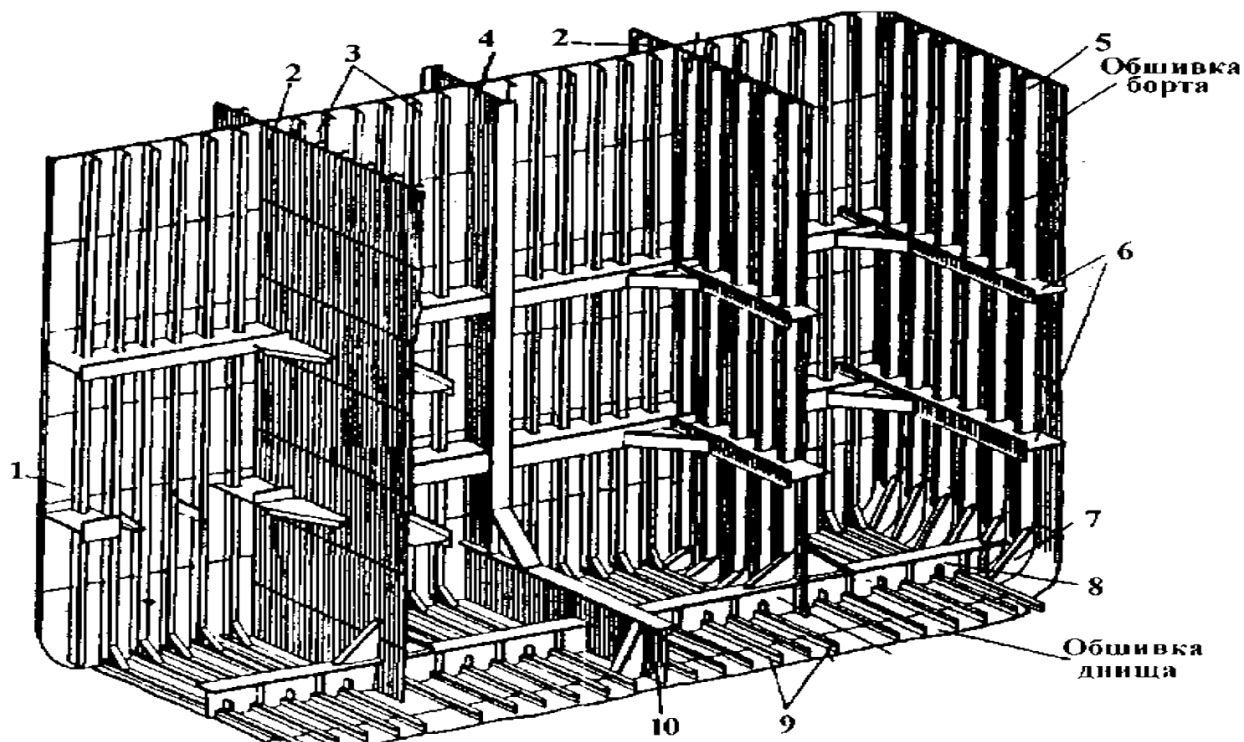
Конструкция главных плоских нефтенепроницаемых поперечной и продольных переборок танкера:
